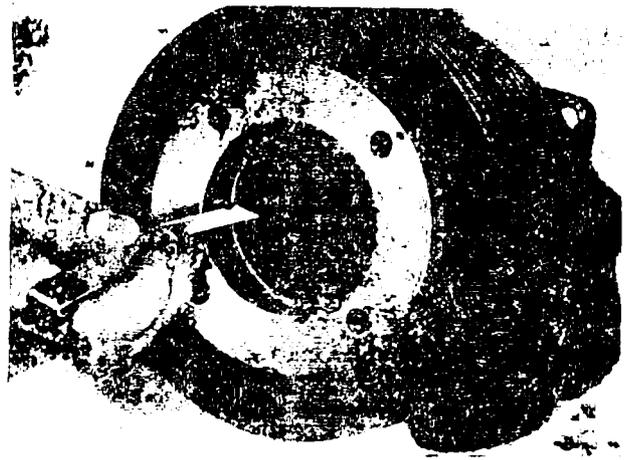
Messen des Kolbenring-Stoßmaßes mittels Fühllehre
